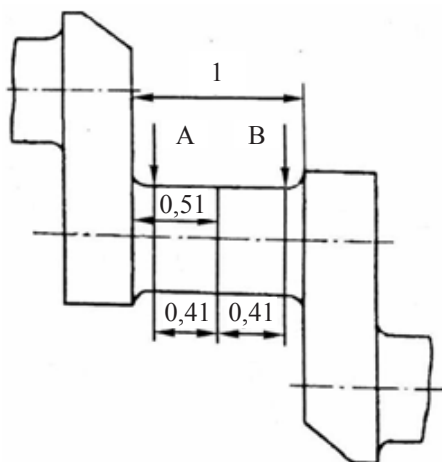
Схема замірювання биття корінної шейки колінчатого вала
